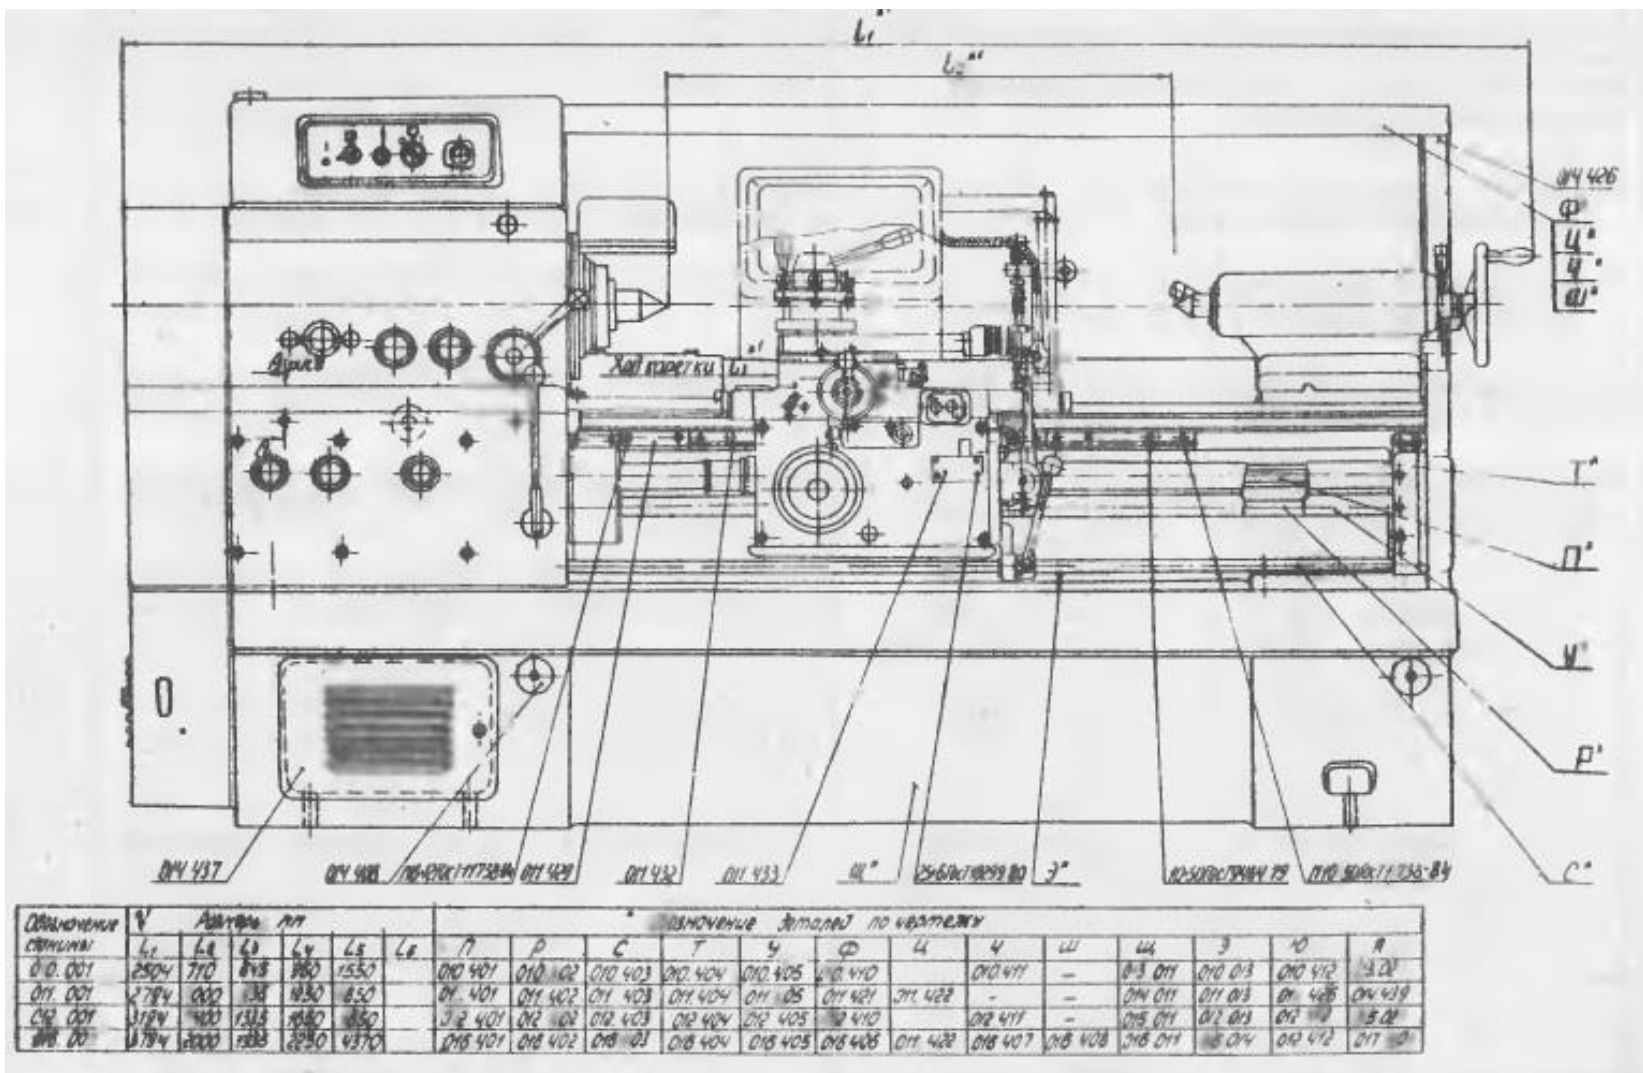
Номера деталей на чертежах следует читать с приставкой «16к20» - для узлов 010, 011, 012, 016, 020, 040, 041, 050, 080; «16Б20П» - для узлов 030, 061, 070. Например, если деталь обозначена 030. 401, следует читать 16Б20П.030.401
